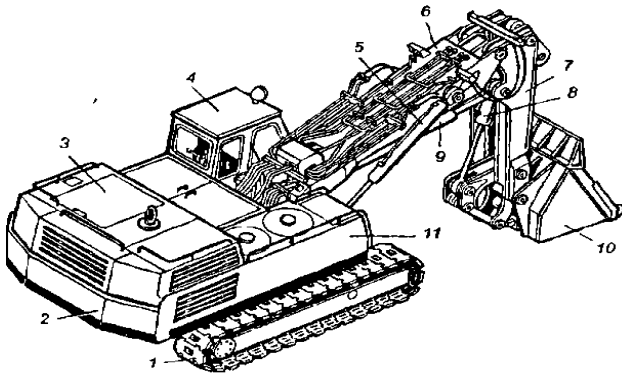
Устройство экскаватора с рабочим оборудованием прямая лопата:
